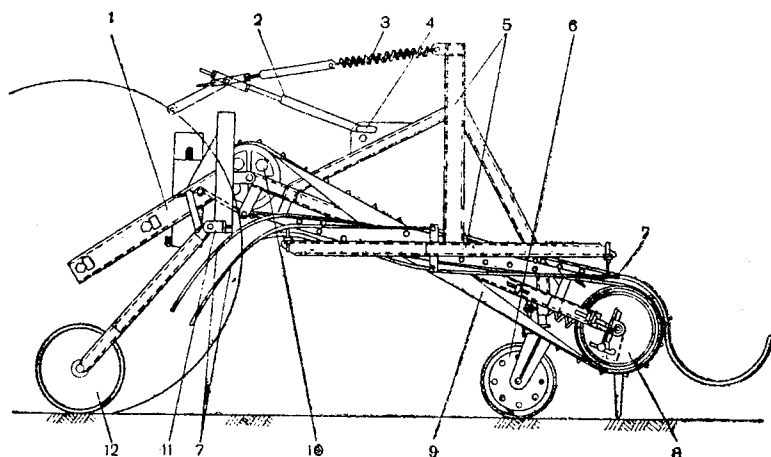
Общий вид подборщика-оборачивателя ОСН-1:
